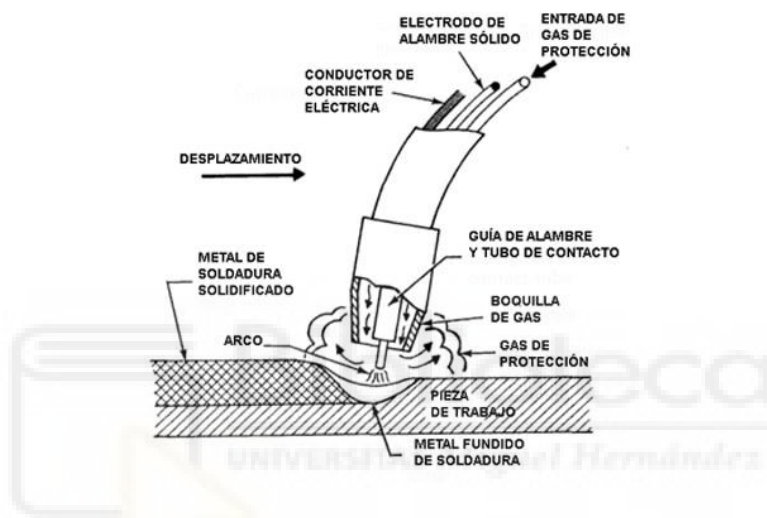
Antorcha de soldadura MIG/MAG
